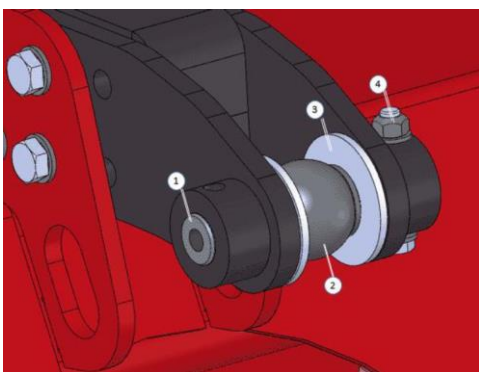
Крепление верхнего рычага мульчирующей фрезы
